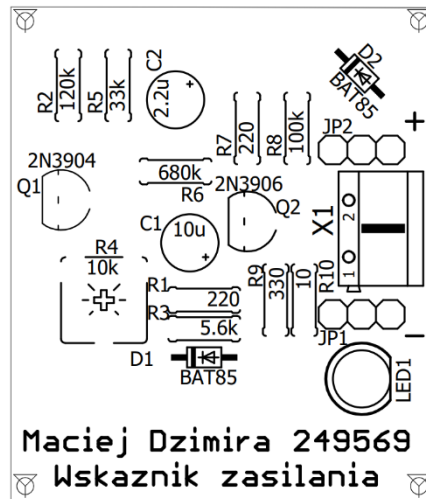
Rozmieszczenie elementów na płytce PCB (skala 1,5:1)
